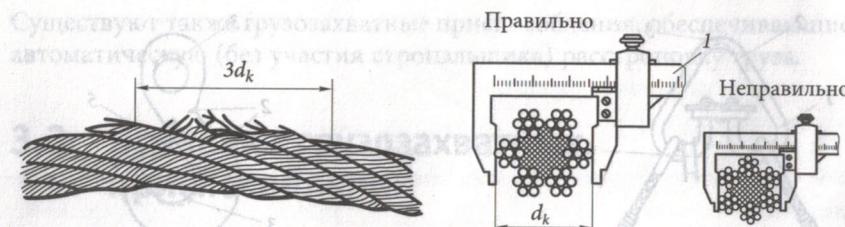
Браковка стропа при наличии обрывов проволок:
